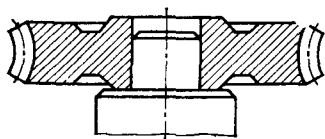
Схема установки колеса червячной передачи при нарезании зуба — неправильная
